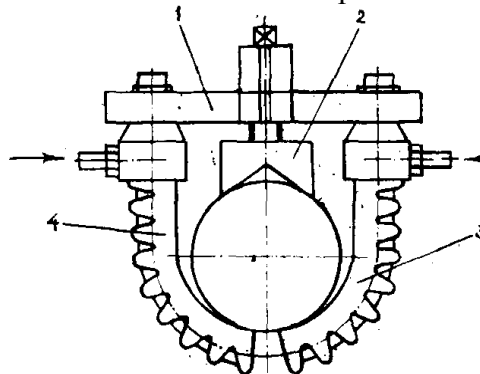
ЗП з еластичними камерами, що звиваються
